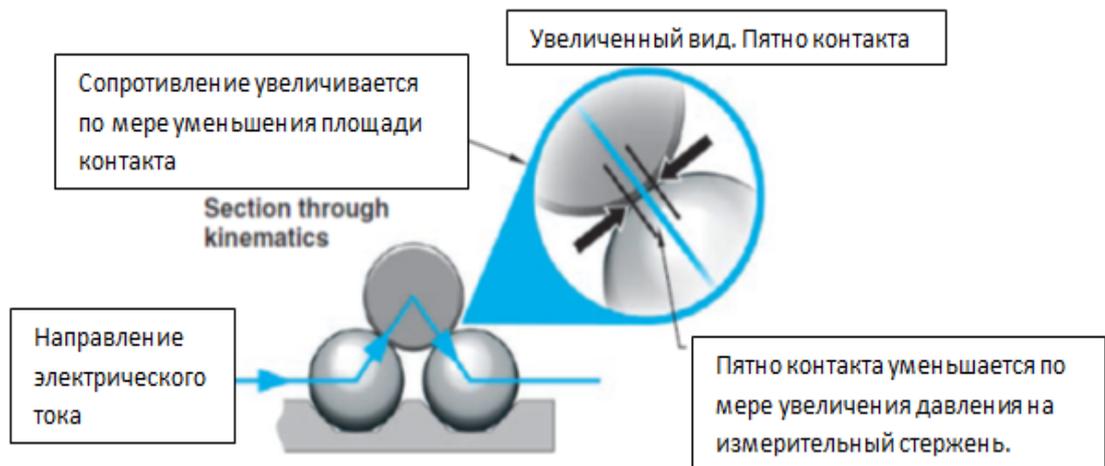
Схема сферической опоры и принципа измерения сопротивления
